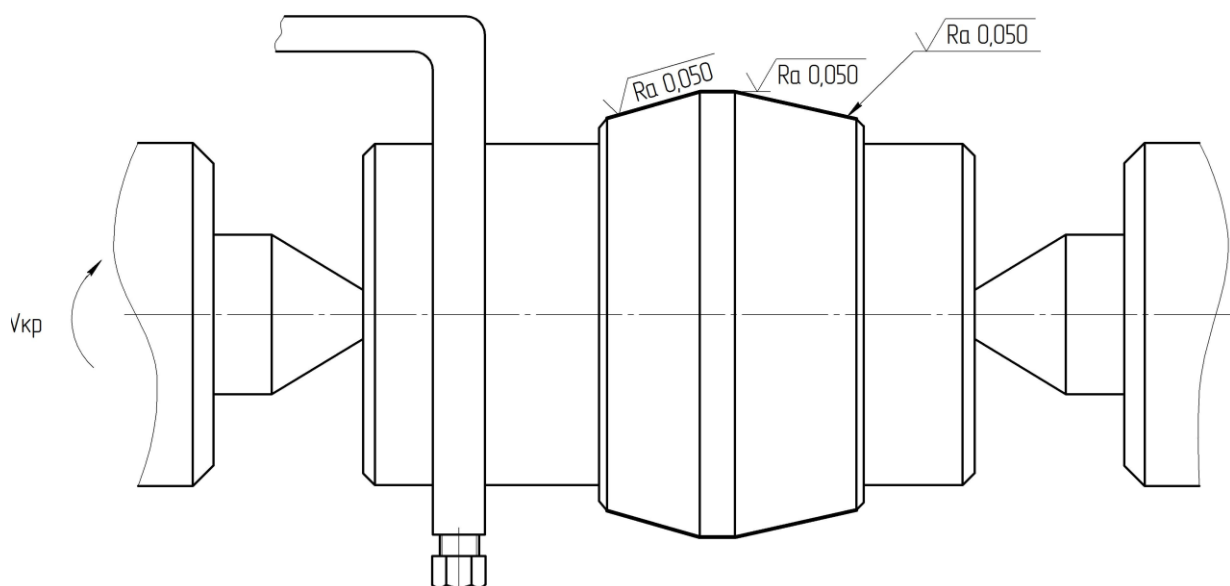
Схема обробки твердосплавного робочого елемента
